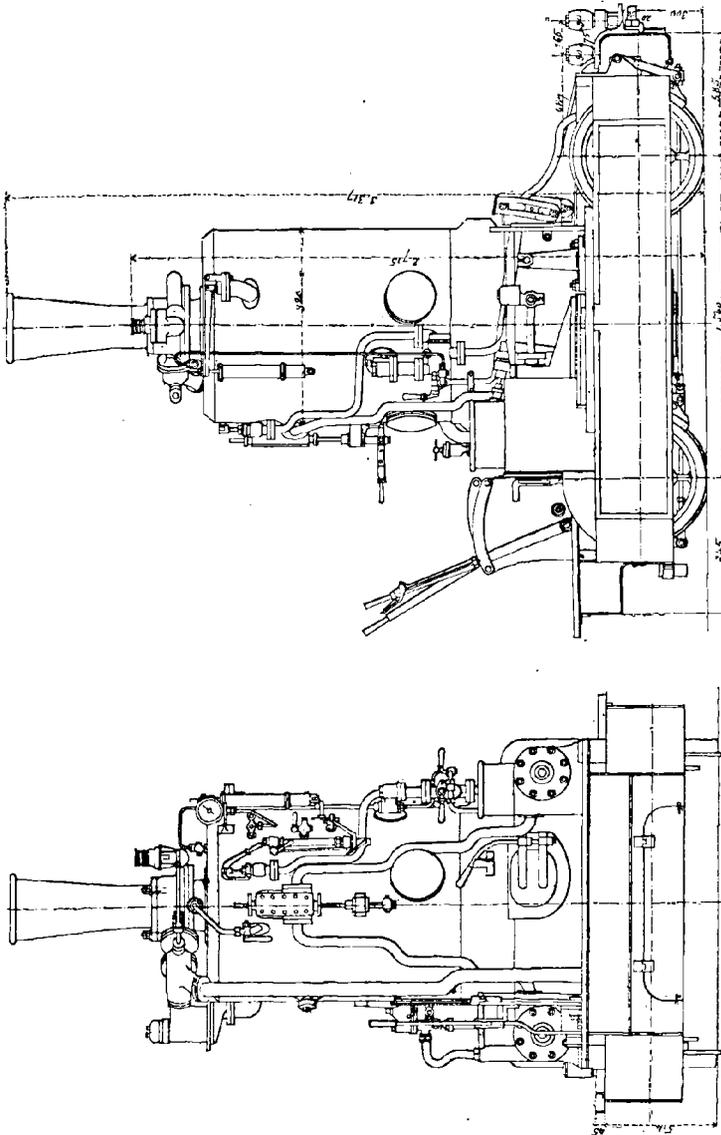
Ensemble de la chaudière et du mécanisme moteur.
